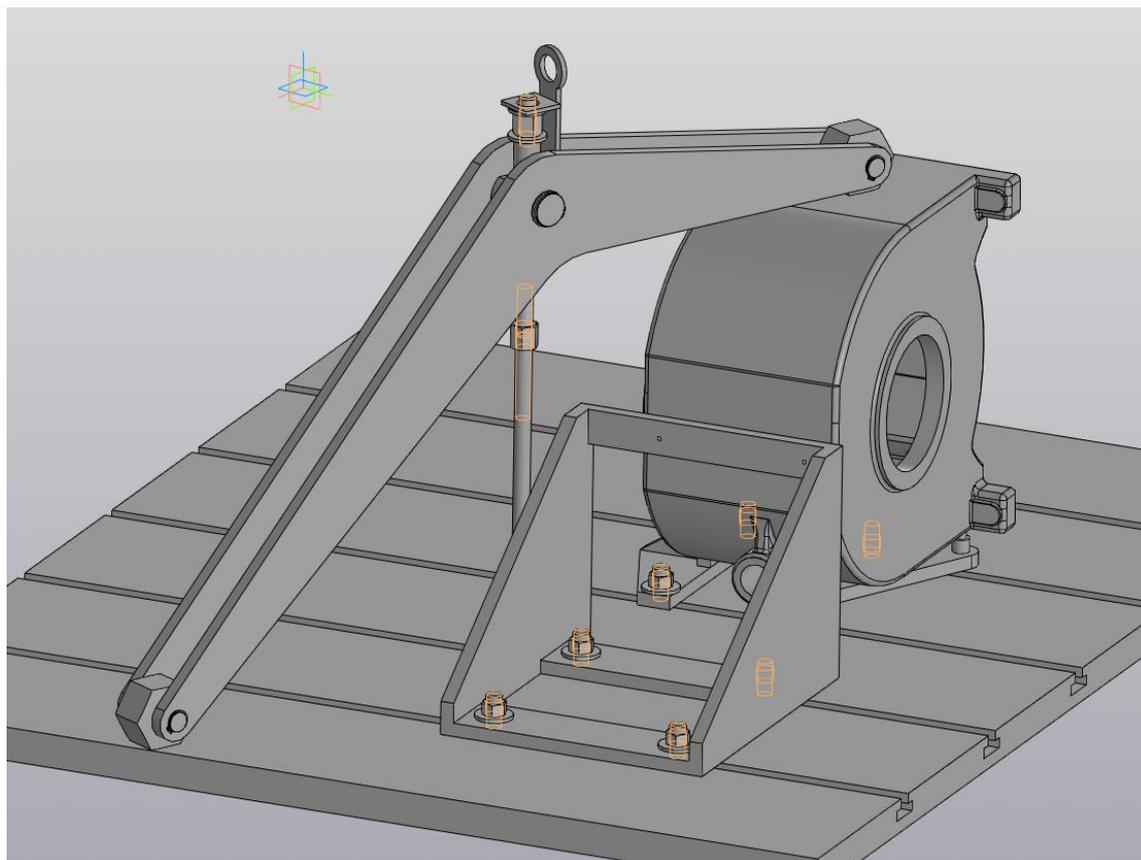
Расположение прижимной планки, базирующих устройств и заготовки на столе
